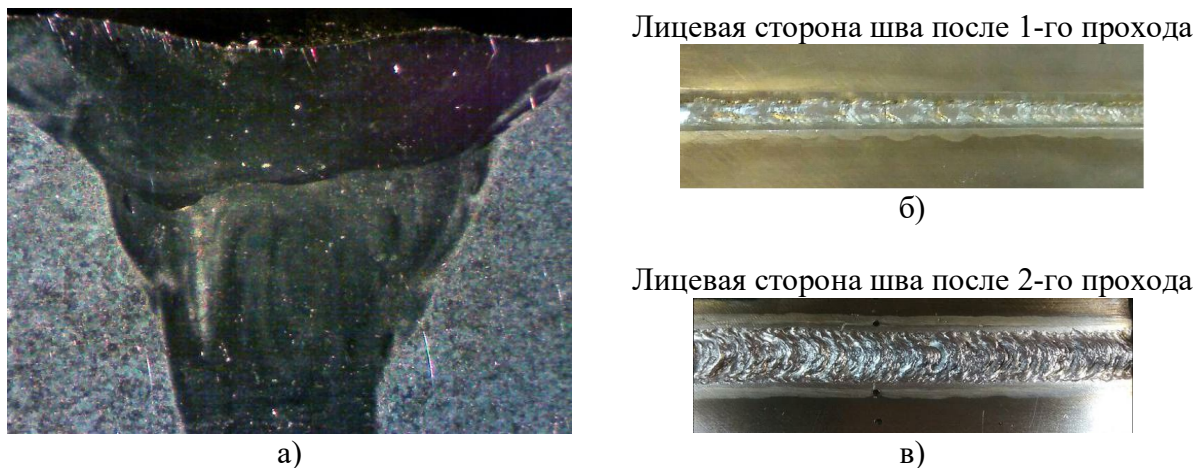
Макрошлиф 2-х проходного сварного шва, выполненного присадочной проволокой ЭП533 (а), и внешний вид лицевой стороны шва после 1-го (б) и 2-го проходов (в)
